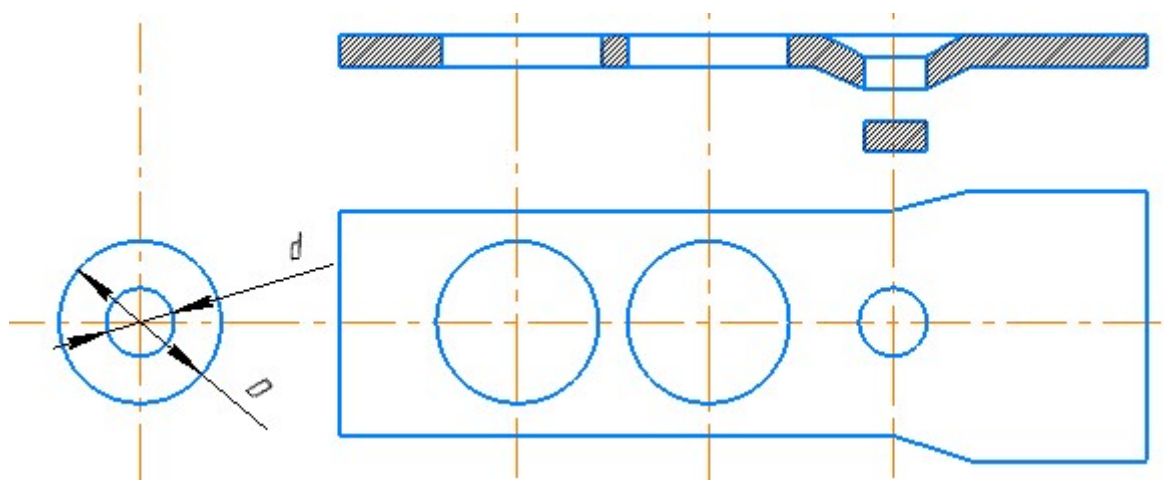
Схема штамповки заготовок тарельчатых пружин с использованием штампа последовательного действия
